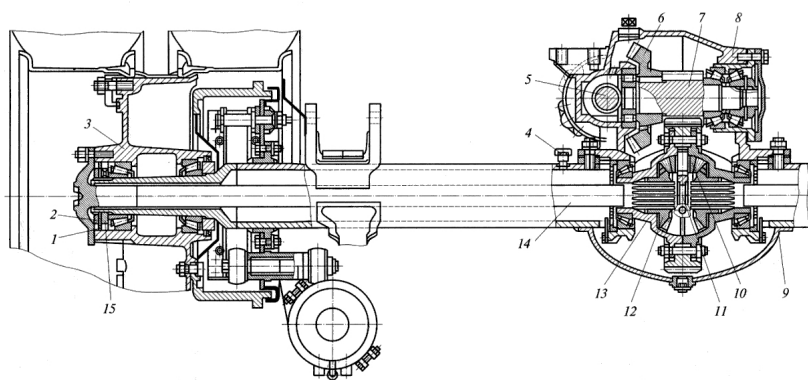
Задний ведущий мост автомобиля КамАЗ: 1 – шайба; 2 – контргайка; 3 – ступица; 4 – сапун; 5 – ведущий вал; 6, 7, 12 – шестерни; 8 – картер главной передачи; 9 – балка; 10 – сателлит; 11 – крестовина; 13 – корпус дифференциала; 14 – полуось; 15 – гайка
